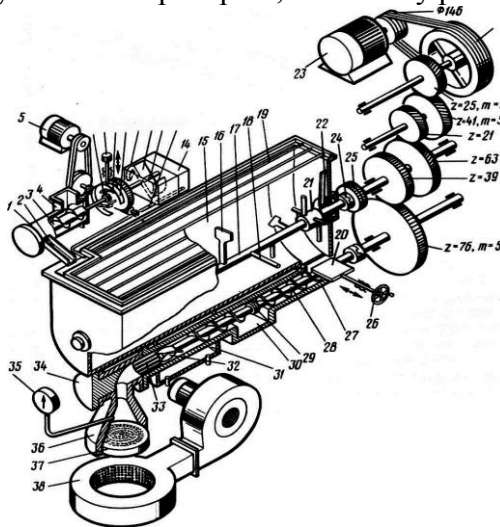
Шнековий макаронний прес ЛПЛ-2М: 1 - корпус дозатора; 2 - лоток; 3, 28 - шнеки; 4 - патрубок; 5 - електродвигун; 6 - храпове колесо; 7 - рукоятка; 8 - двоплечий важіль; 9 - півкільце; 10, 14 - бачки; 11 - кишени крильчатки; 12, 17 - вали; 13 - труба; 15 - однокамерна ємність; 16 - лопатка; 18 - палець; 19 - кришка; 20 - заслінка; 21 - штовхач; 22 - ніж; 23 - електродвигун; 24 - муфта; 25 - зірочки; 26 - маховичок; 27 - пресувальний корпус; 29 - шайба; 30 - пропускний канал; 31 - водяна сорочка; 32 - тризахідна ланка; 33 - канавки; 34 - фланець; 35 - манометр; 36 - пресова головка; 37 - матриця; 38 - пристрій обдувальний
